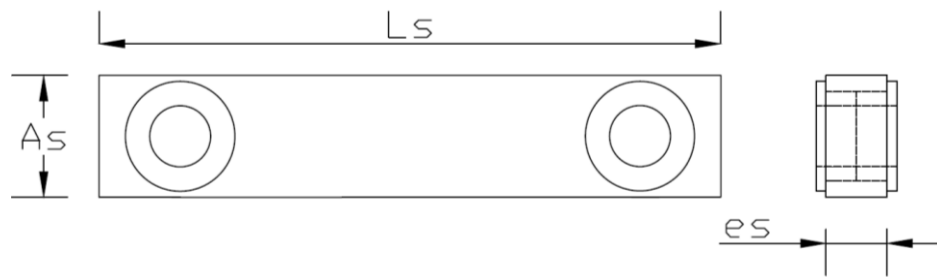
Dimensiones asumidas del soporte para cojinetes
